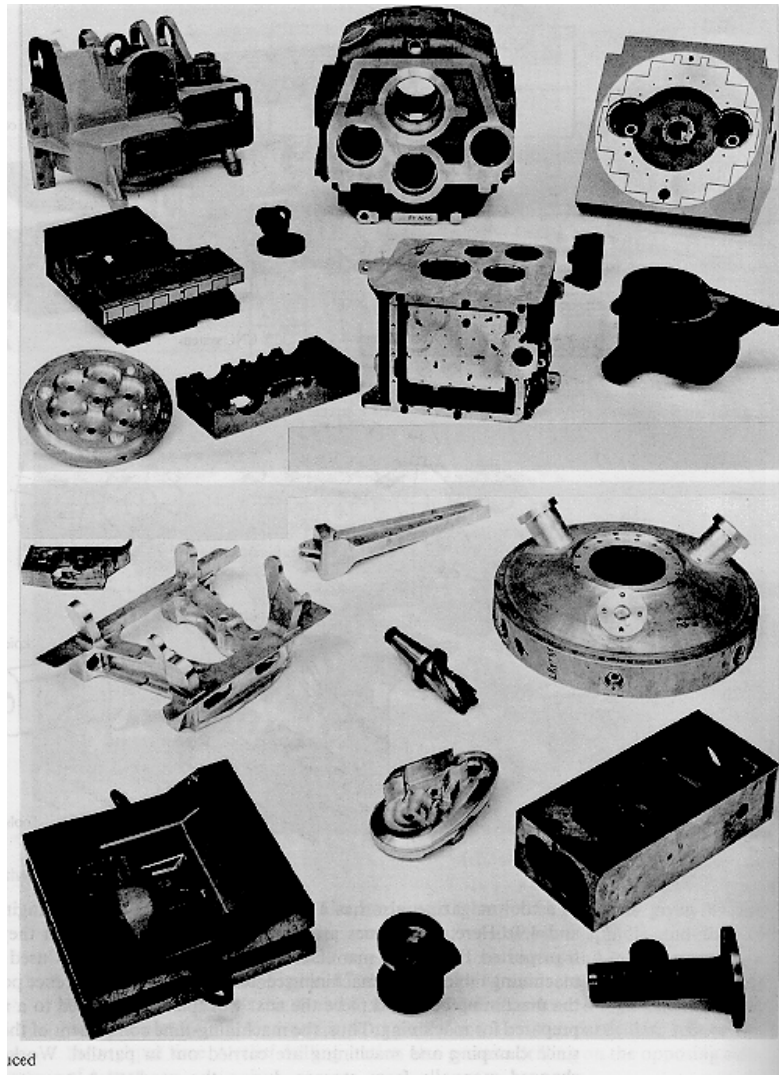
Peças complexas fabricadas num centro de usinagem
